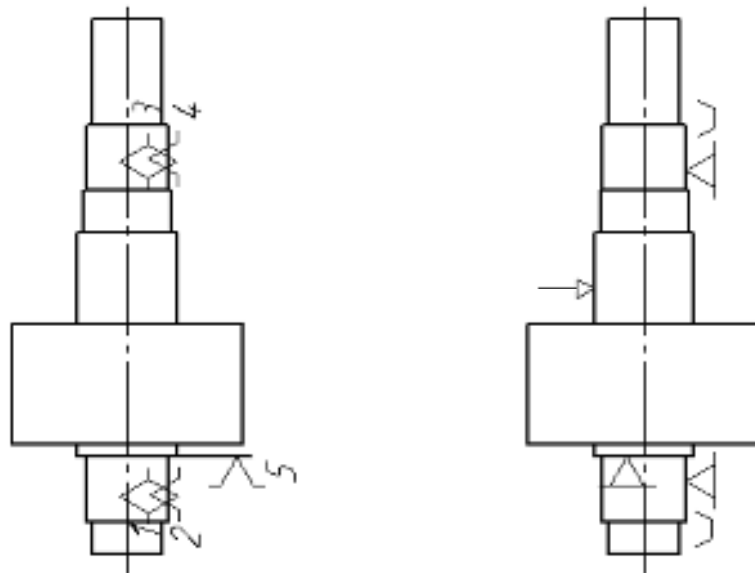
Схема базування і закріплення деталі на координатно-свердильній операції
